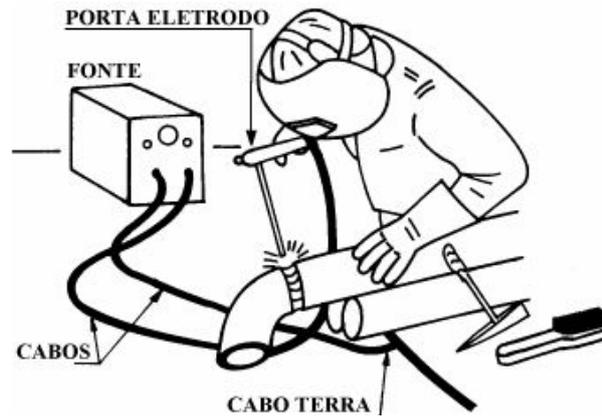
Equipamento para soldadura a ER. Fonte - Paulo Modenesi et al
